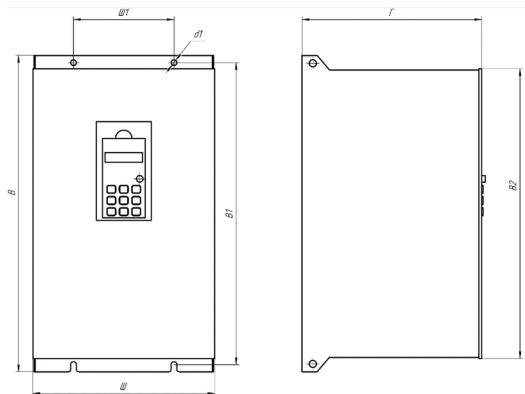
Установочные и габаритные размеры тормозного модуля FCI-BU, типоразмер 2
